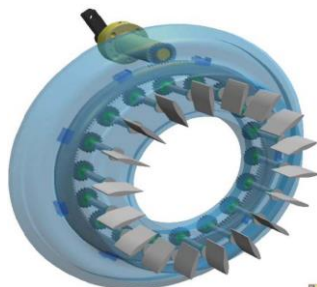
Типовое исполнение ВНА для центробежного компрессора.
